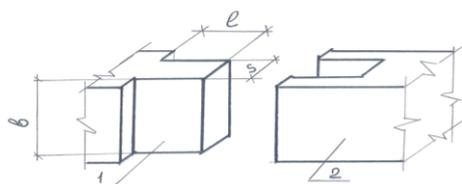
Шиповое соединение: 1 – шип, 2 – проушина, l – длина шипа, b – ширина шипа, s – толщина шипа
